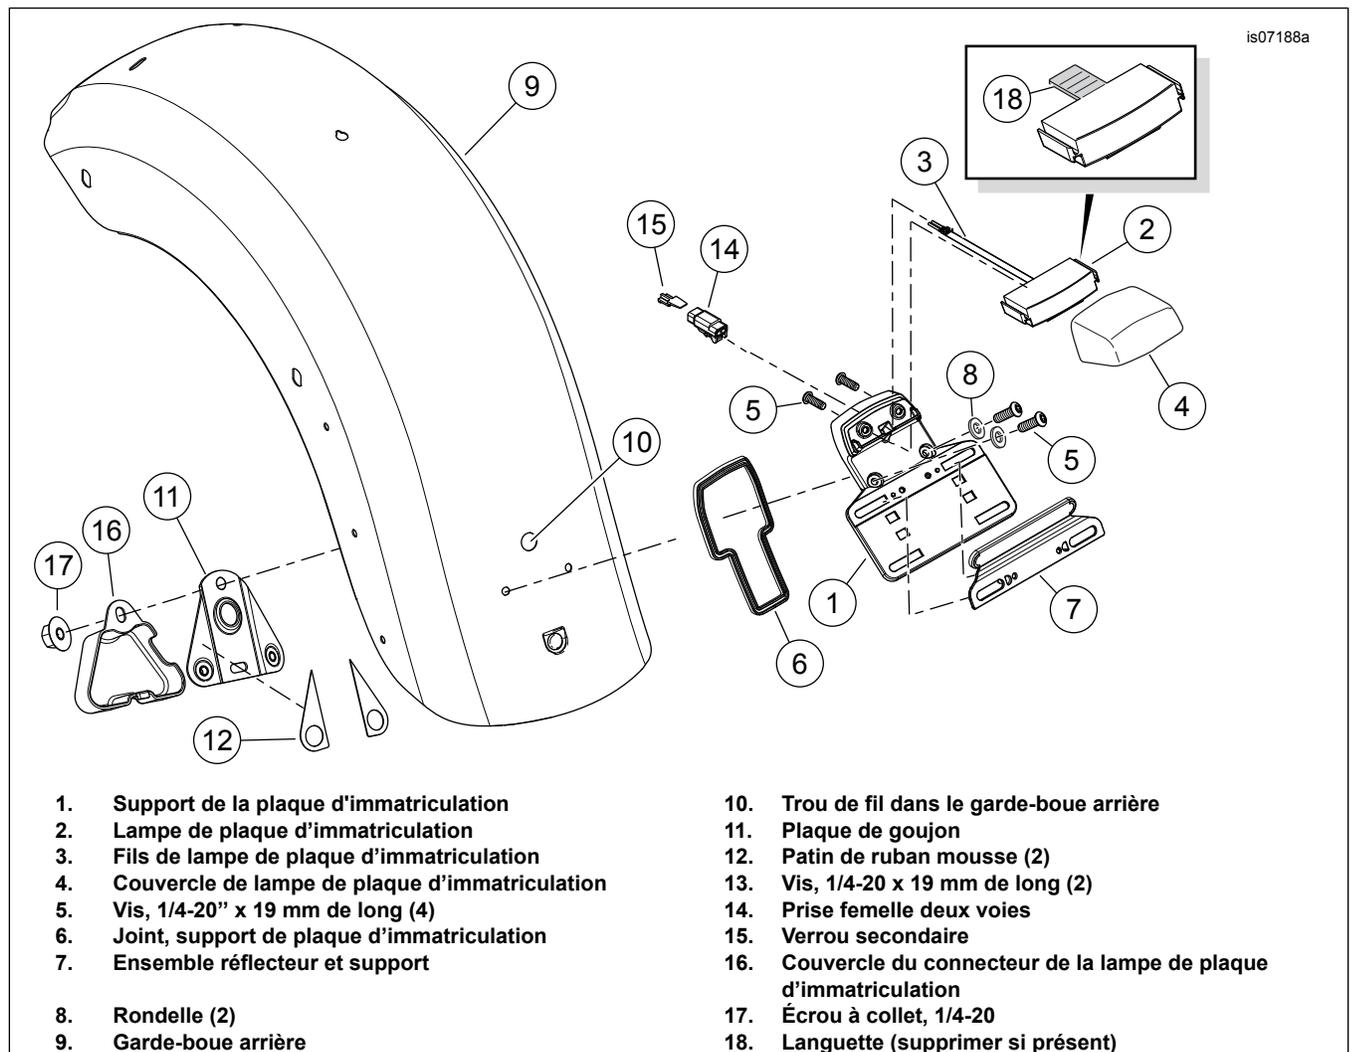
Installation de la lampe et du support de plaque d'immatriculation
